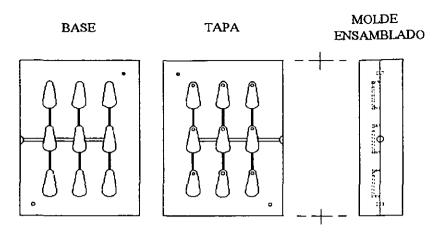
Molde multiple para inyección en molde cerrado.
